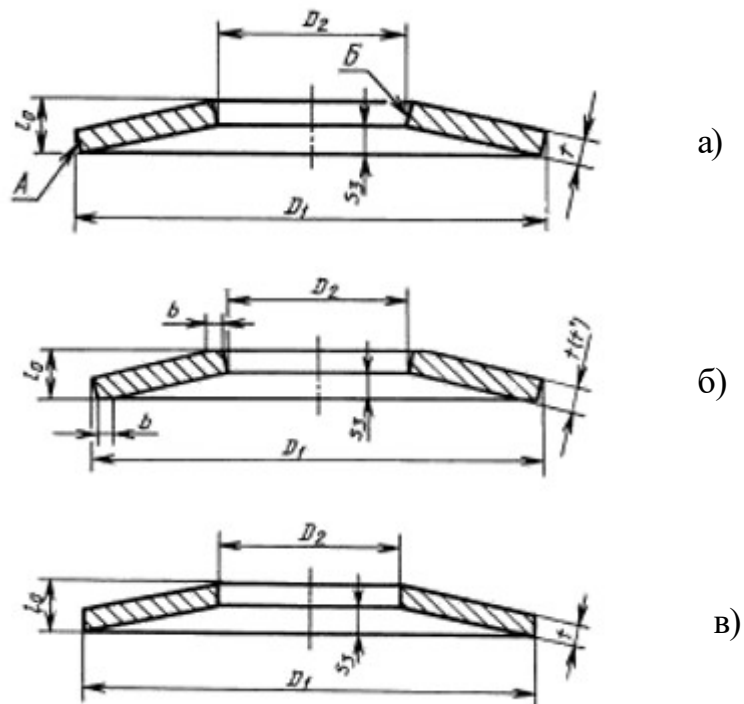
Розрахункова схема тарілчастої пружини
